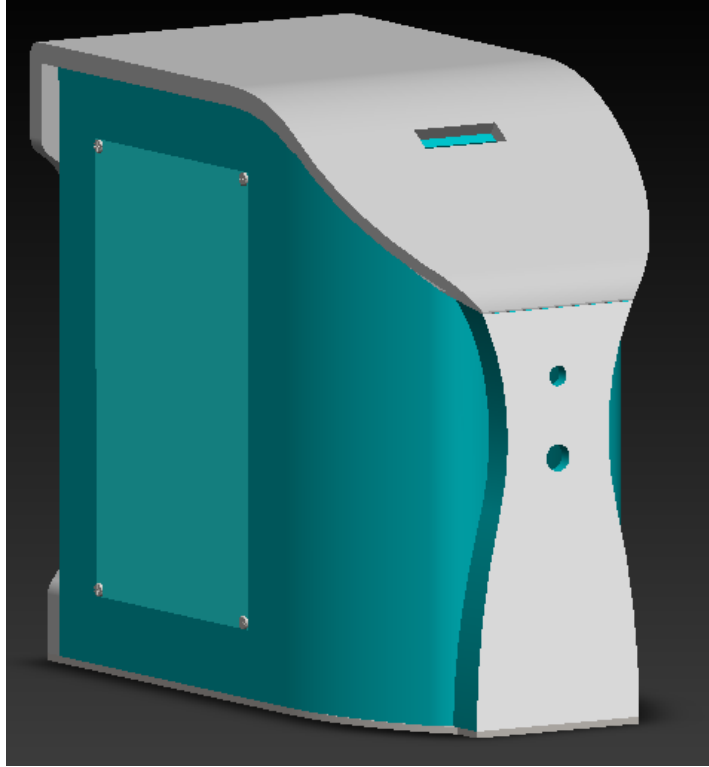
11. Vista frontal máquina extractora de folículos diseñada en Solid Works.
